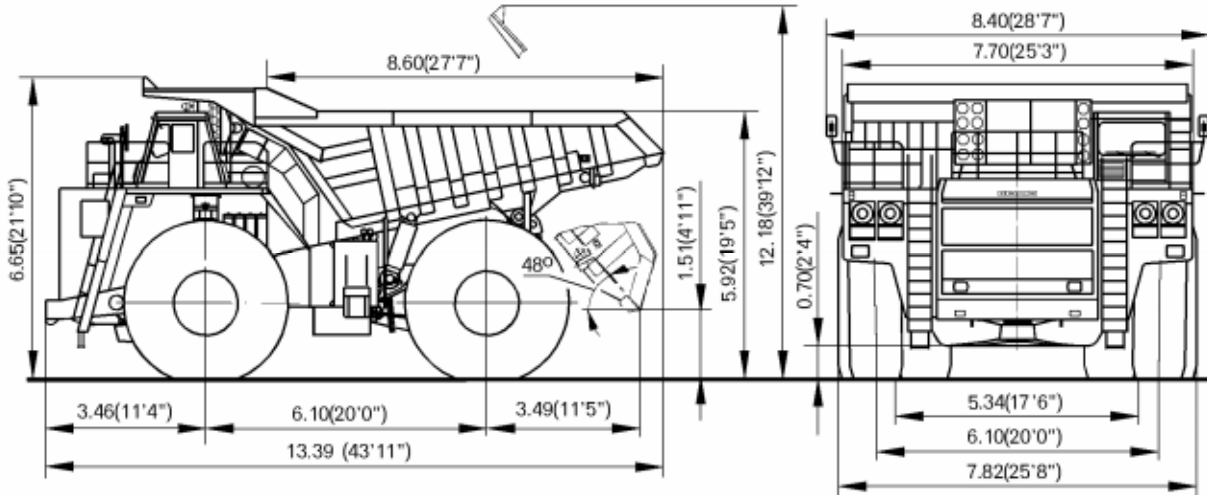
Карьерный самосвал БелАЗ-75306. Габаритные размеры
